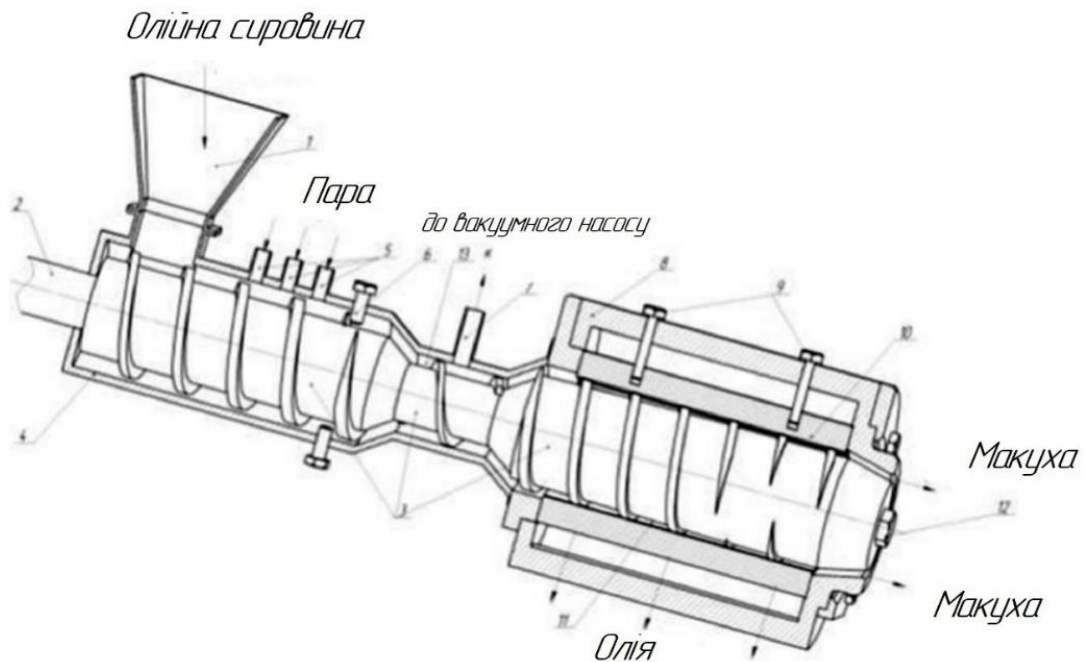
Екструдер олійно-жировий: 1–завантажувальна воронка, 2–вал, 3 – втулка с гвинтовими навивками, 4– екструзійна камера, 5–форсунки, 6, 12– гвинт, 7–патрубок, 8–корпус, 9–болт, 10– зеєрні пластини, 11– зеєрна камера, 13 – камера вакуумування.
